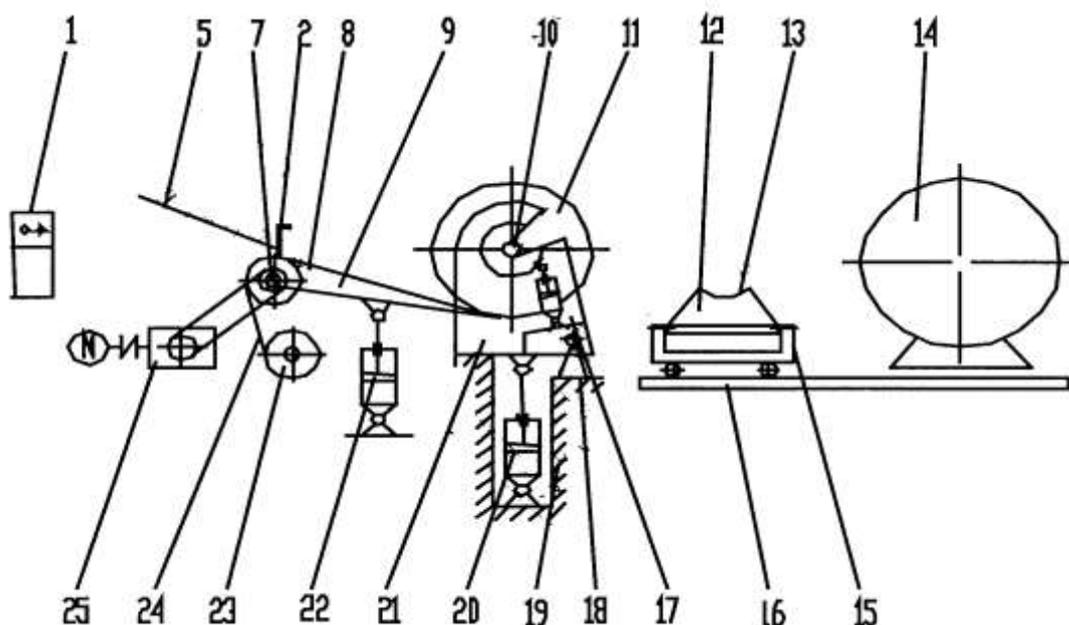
Пакетоформирующая машина: 1 – пульт управления; 2 – упор; 5 – склизы; 7 – звездочка; 8 – гибкие прокладки; 9 – поддерживающий рычаг; 10 – рычаг сбрасывателя; 11 – барабан с заготовками; 12 – колесная платформа; 13 – опора; 14 – автоклав; 15 – основание; 16 – фундамент; 17, 20, 22 – гидроцилиндры; 18, 19 – основание; 21 – сбрасыватель; 23 – кассета гибких прокладок; 24 – резиновая лента; 25 –
